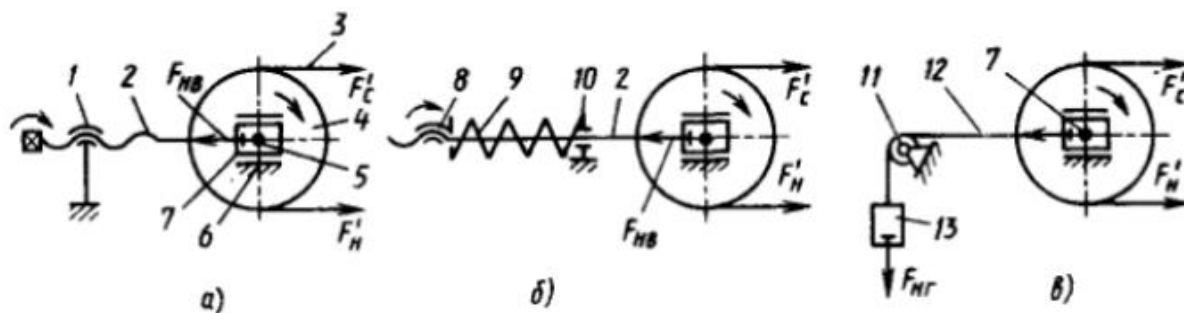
Схема натяжних пристроїв стрічкового конвеєра а - гвинтове; б – гвинтове з пружиною; в - вантажне 1 - гайка; 2 - гвинт; 3 - конвеєрна стрічка; 4 - барабан; 5 - вісь; 6 - направляюче; 7 - повзун; 8 - гайка; 9 - пружина; 10 - упор; 11 - нерухомий блок; 12 - канат; 13 - вантаж
